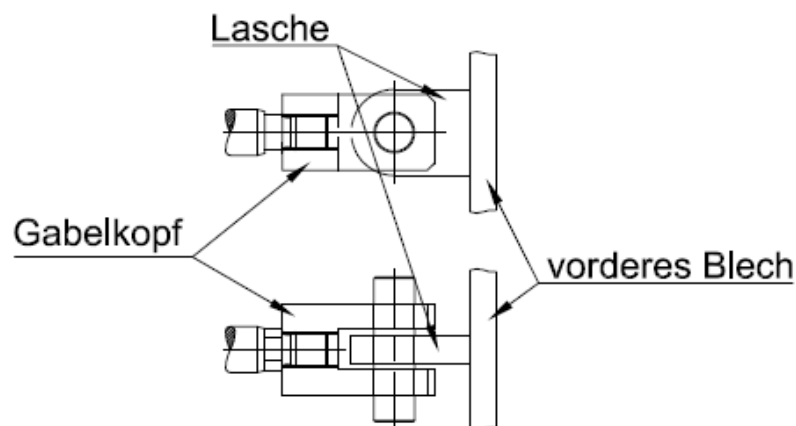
BG11; Detail Befestigung Lasche-Gelenkkopf
